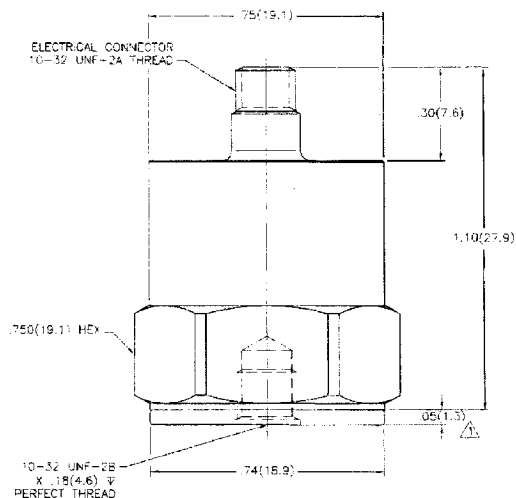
Schéma de l'accéléromètre 352B de PCB
